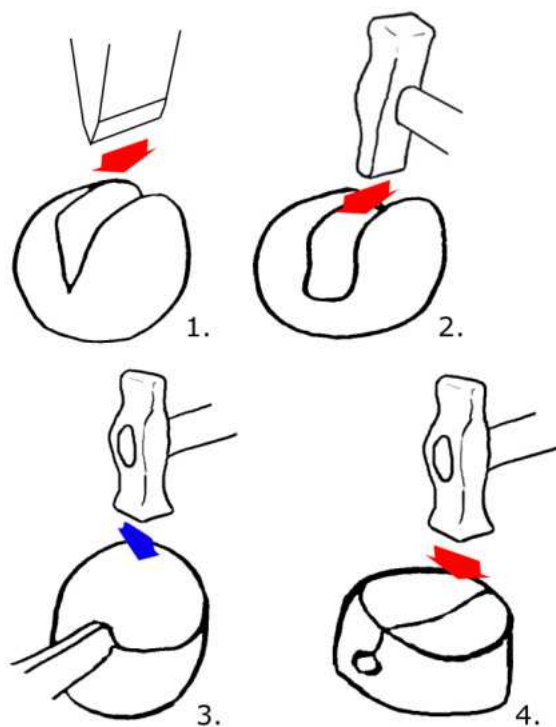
Procédé par section et fermeture par soudage. Dessin F. Cognot.
